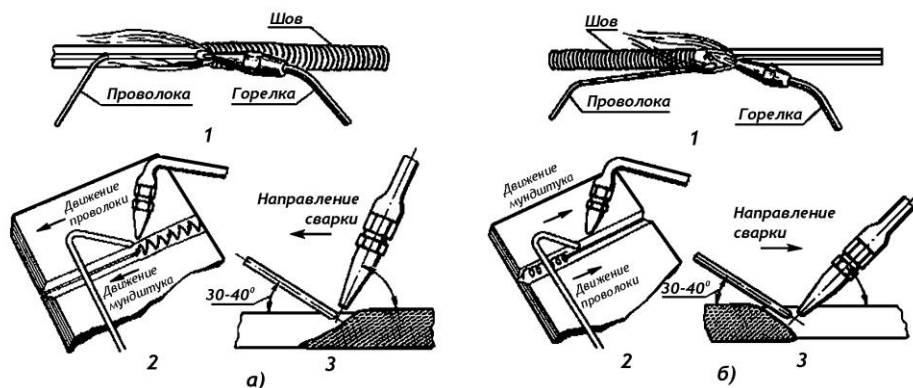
Способы сварки, где 1 – момент сварки, 2 – схемы движения мундштука и проволоки, 3 углы наклона мундштука и проволоки
